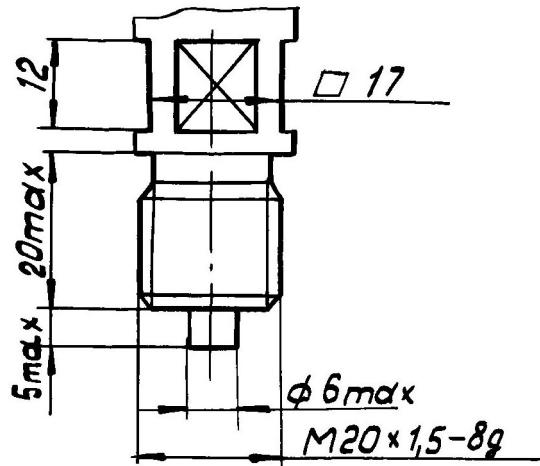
(лист 1 из 2) – Габаритные и присоединительные размеры приборов
